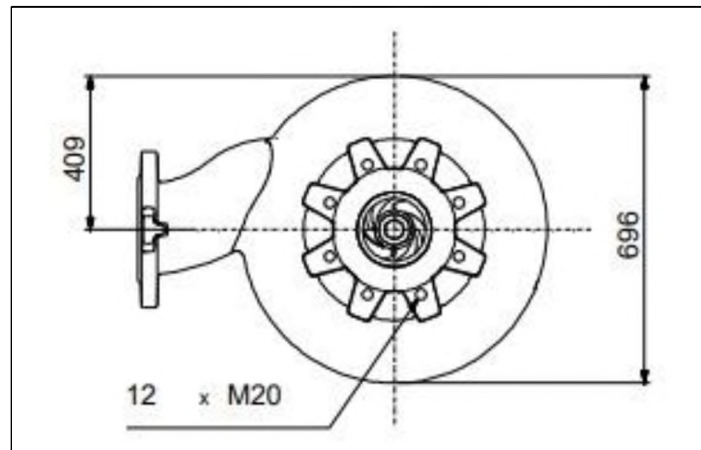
Vista en planta de Bomba tipo seleccionada (fuente: Grundfos)
